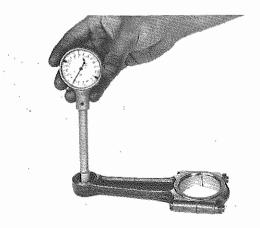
Misurare il gioco radiale Radial clearance measurement
